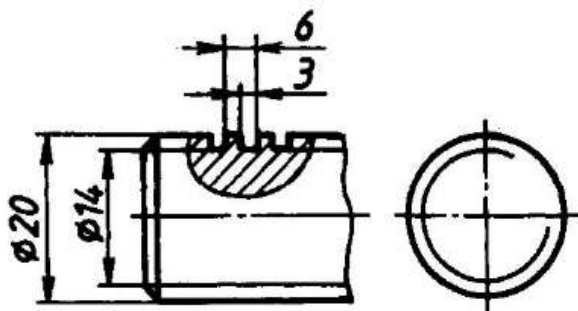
14 – Чертеж детали с прямоугольной резьбой
